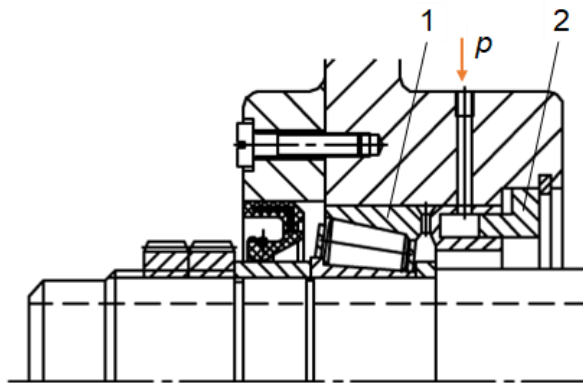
Задня опора ШВ токарного верстата з ЧПК з керованим натягом
